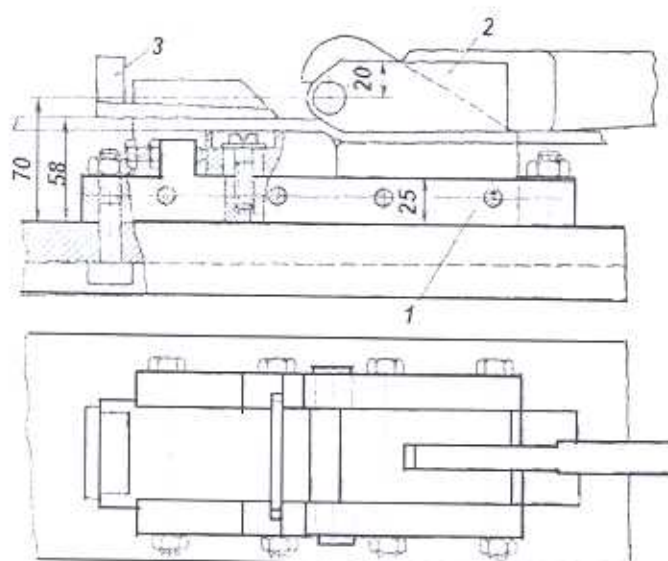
Приспособление для изгиба меди статорной обмотки:
